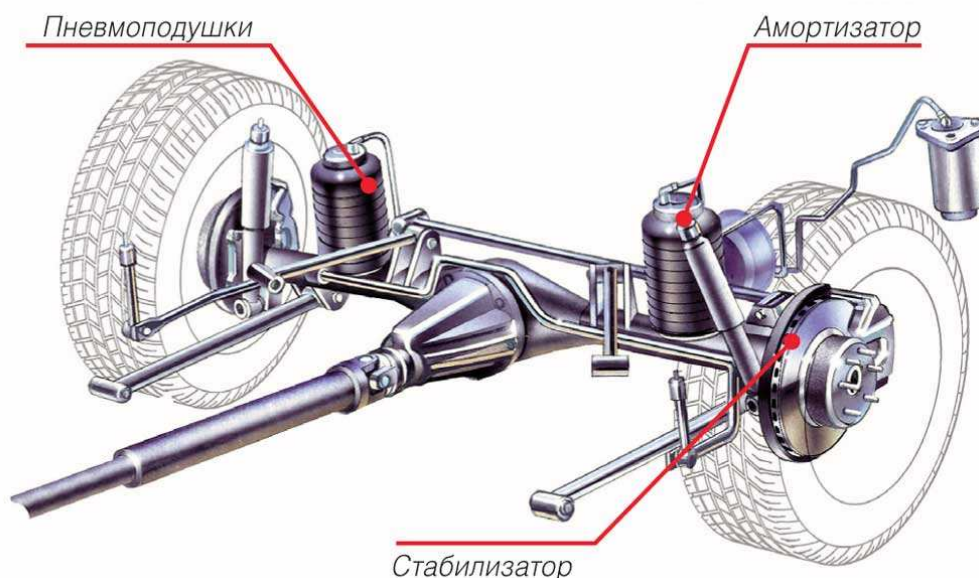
Предлагаемая конструкция пневматической подвески для Волжанин 3290
